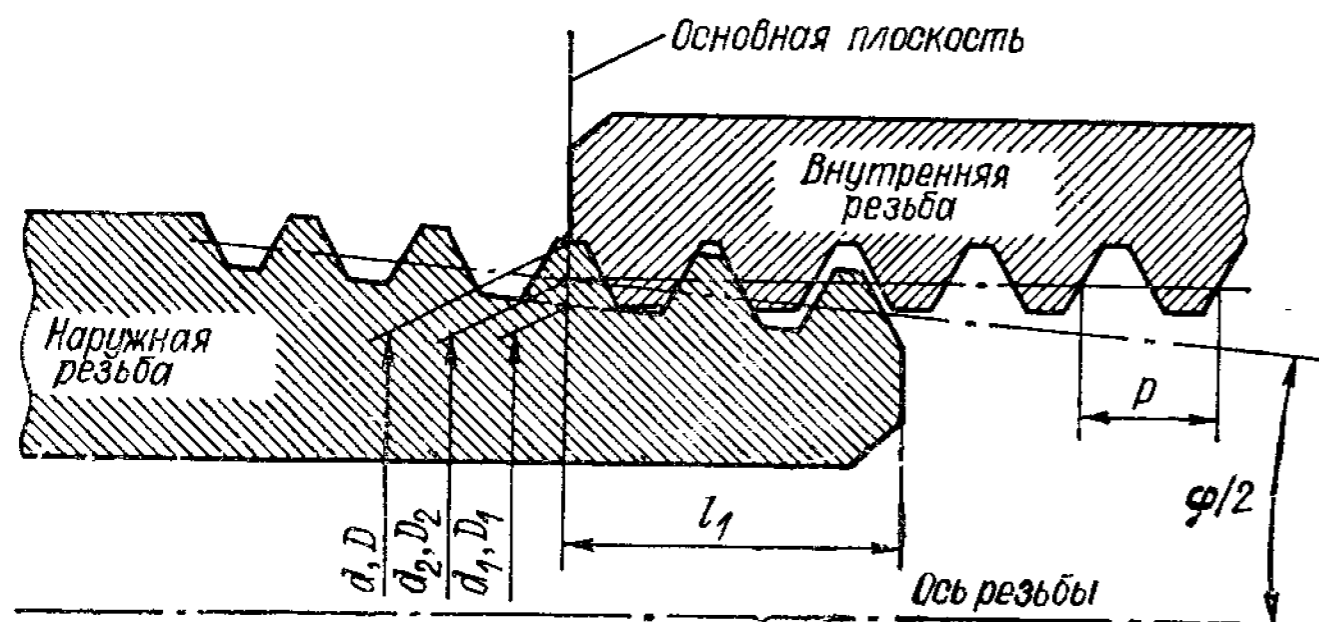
Соединение наружной конической с внутренней цилиндрической резьбой
